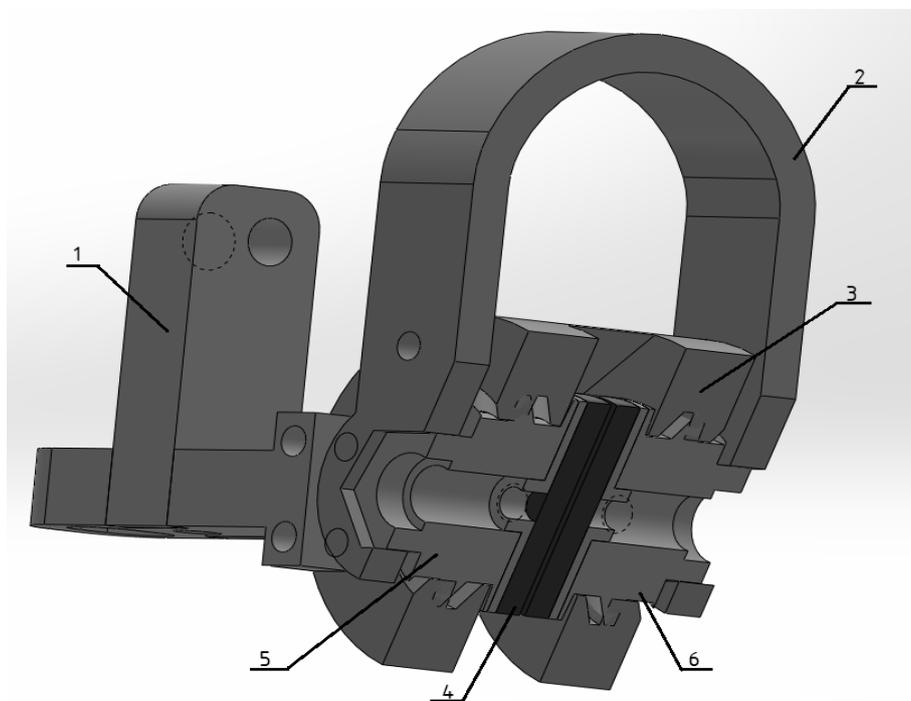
Механический дисковый тормоз [5]: 1 – крепление тормоза; 2 – скоба; 3 – корпус; 4 – тормозная колодка; 5 – левый прижимной винт; 6 – правый прижимной винт
